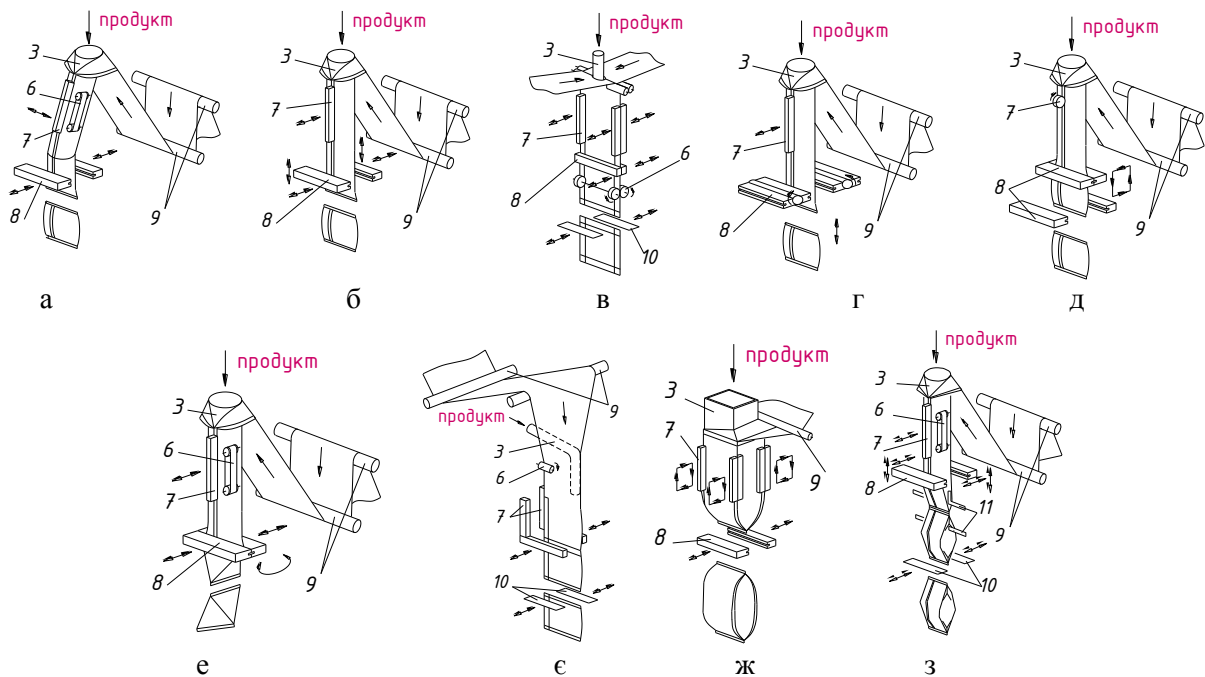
Типи компонок пакувального блоку модулів: а) з нахиленим рукавоутворювачем; б) з протяжними губками зварювання і відрізання; в) з протяжними роликками; г) з роторними губками поперечного зварювання; д) з двома парами губок поперечного зварювання; е) з поворотними губками поперечного зварювання; є) із об'єднаними губками поздовжнього і поперечного зварювання; ж) з протяжними губками поздовжнього зварювання; з) з механізмом утворення складок;
